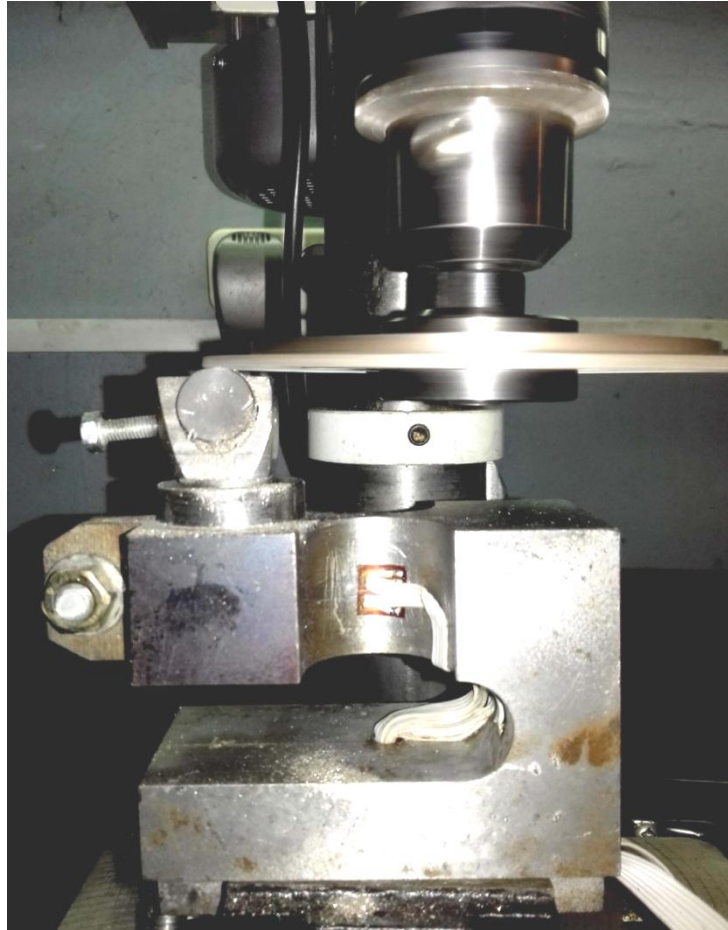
Испытания резцов на поверхностное разрушение при трении о рабочую поверхность алмазного отрезного диска
